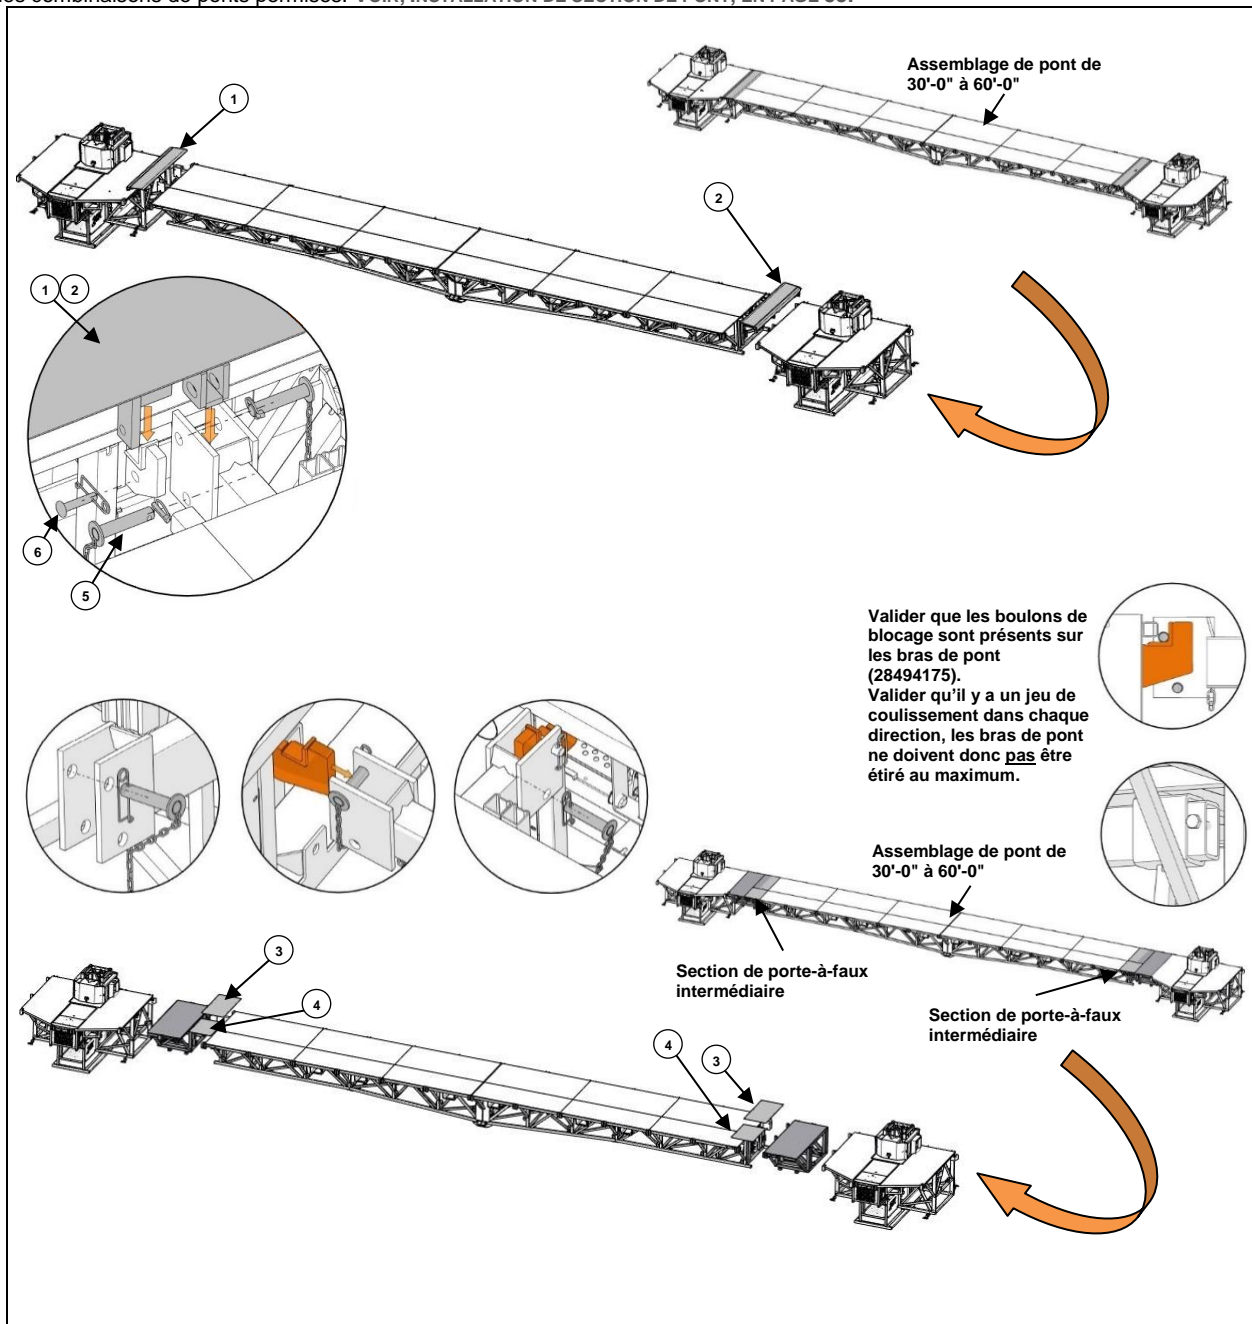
Installation d'assemblage de pont 30'-0" à 60'-0" sur unité élévatrice et/ou PAF intermédiaire
